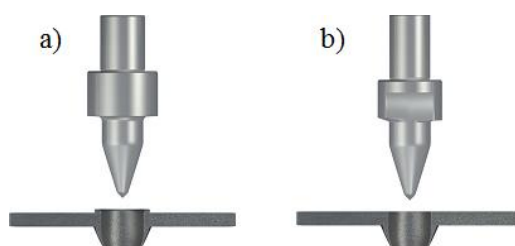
Postup výroby závitů metodou Thermdrill [24]
